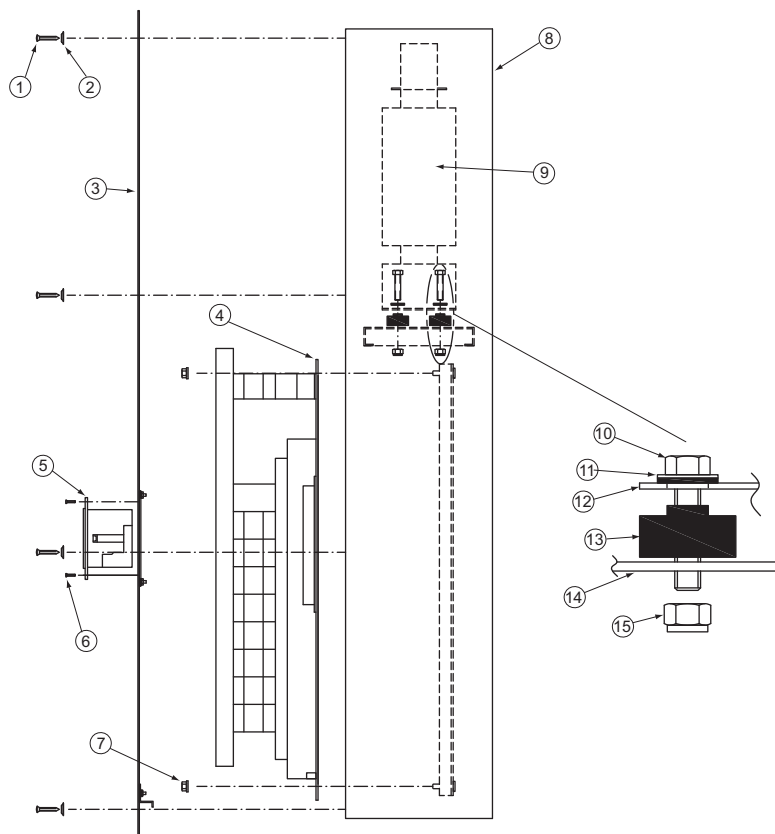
Assemblage—Panneau SIP, 3 et 5 kVA
